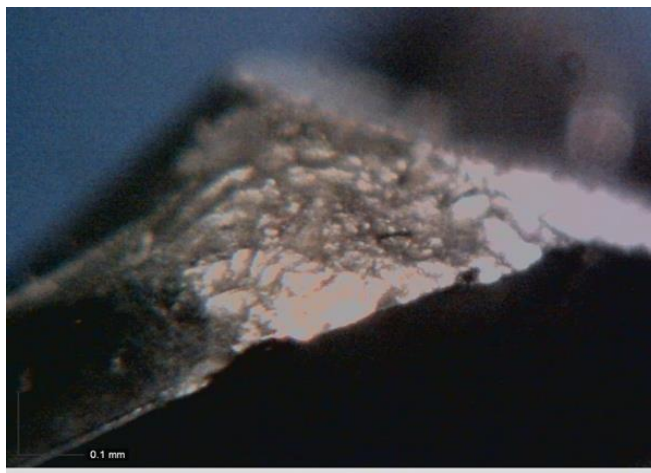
Vista lateral do desgaste da superfície de flanco
